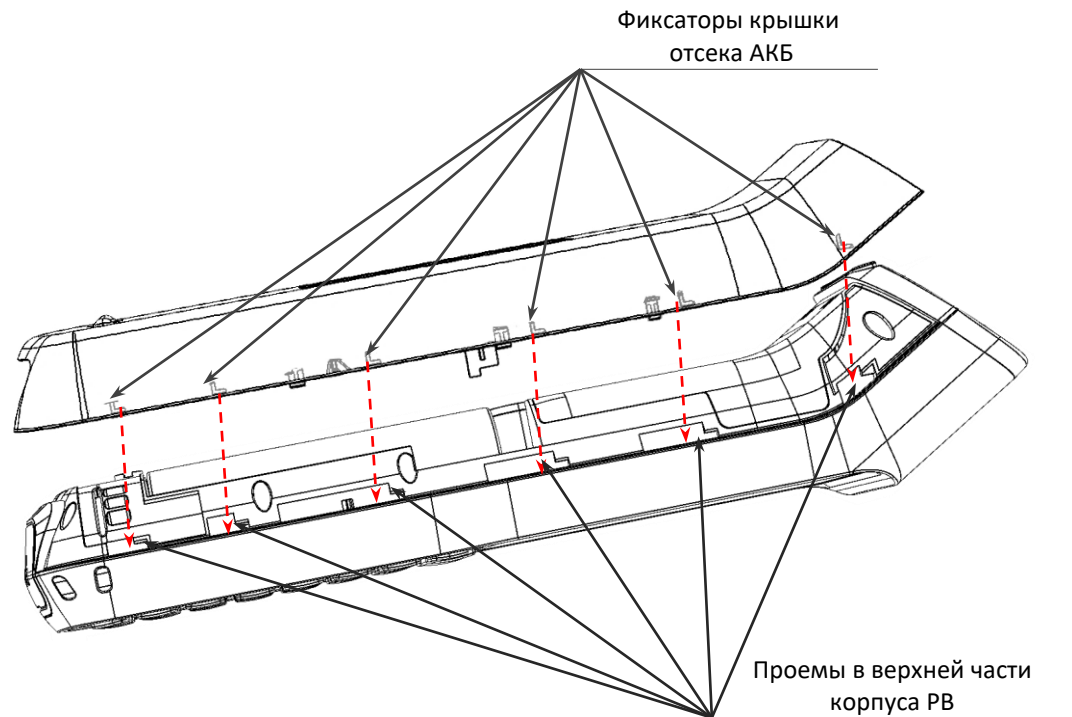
Установка крышки отсека АКБ на верхнюю часть корпуса (расположение фиксаторов и проемов)
